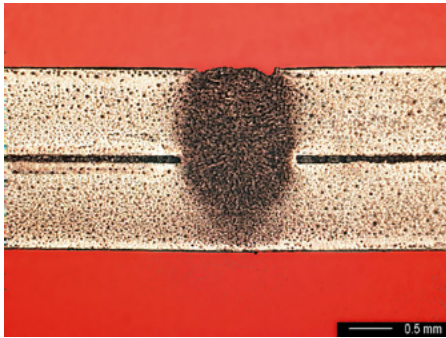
Profil einer geregelten Einschweißung am Überlapp-Stoß
